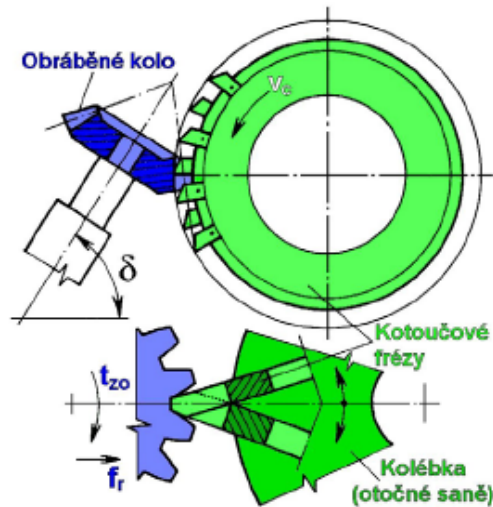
Frézování ozubení kuželového kola kotoučovou tvarovou frézou
